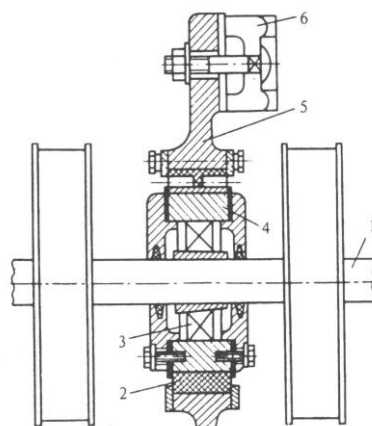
Конструкция виброопоры главного вала машины ПК-100: 1 – главный вал; 2 – резиновая втулка; 3 – шарикоподшипники; 4 – опорная втулка; 5 – кронштейн; 6 – промежуточная стойка остова.
